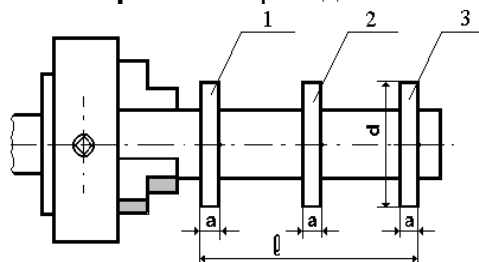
Схема для проверки обеспечения токарным станком точности геометрической формы: 1, 2, 3 – пояски; *a* – ширина пояска; *d* – диаметр пояска
